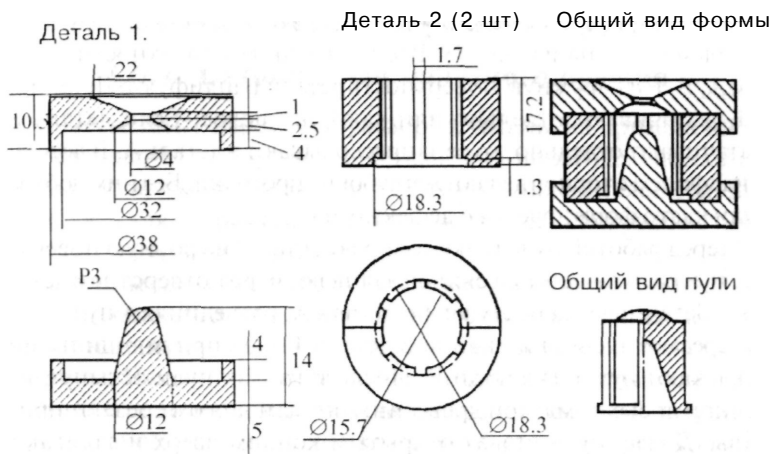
Пулелейка для колпачковых пуль 12-го калибра
